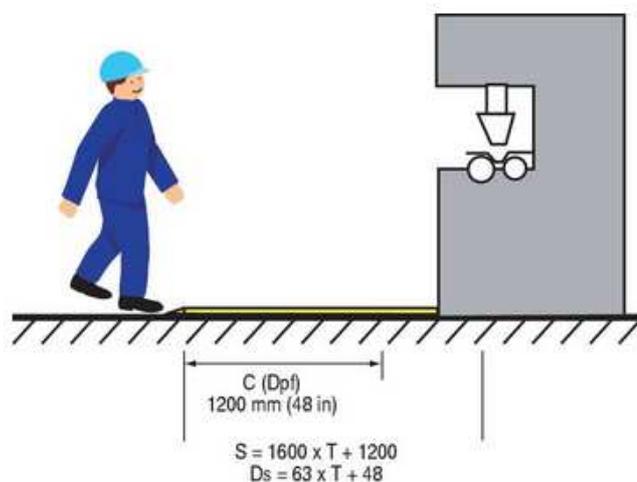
Distanza di sicurezza con pedana montata su pavimento. [2]
